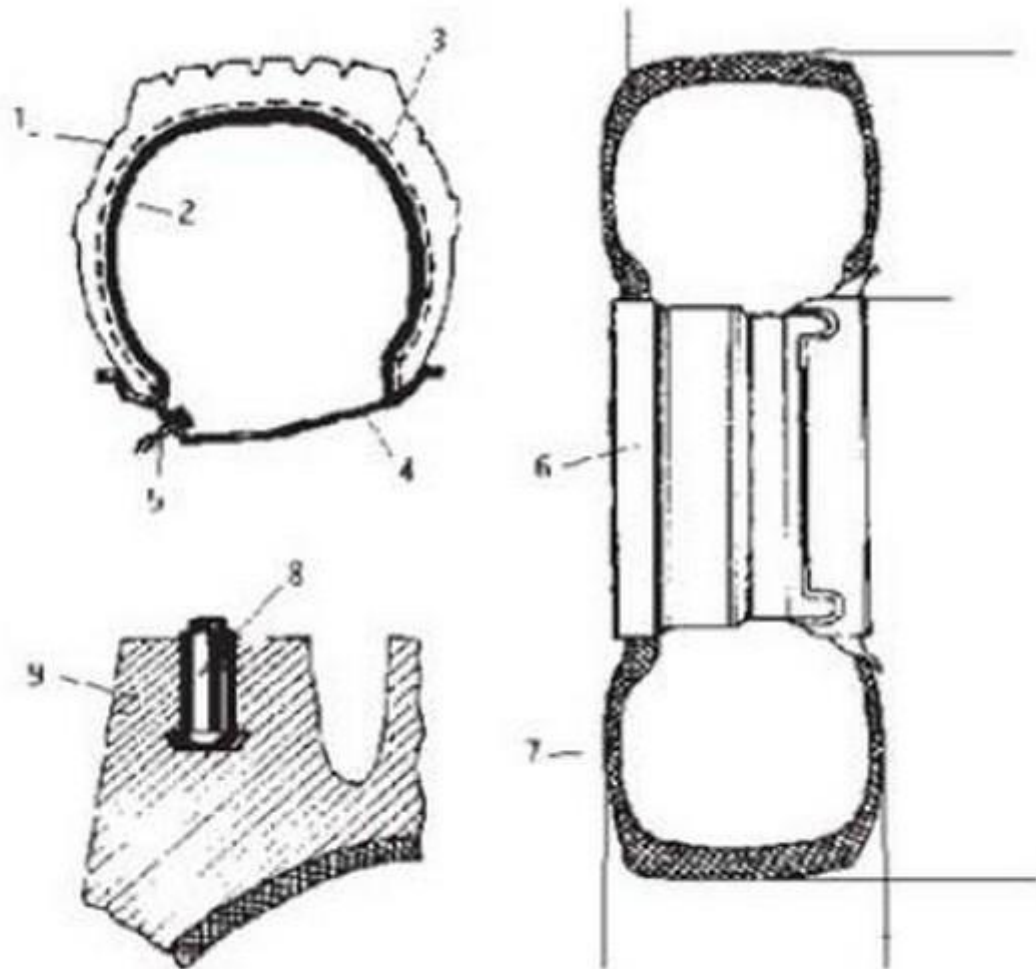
Шина автомобиля: 1 — покрышка; 2 — ездая камера; 3 — корд; 4 — лента обода; 5 — вентиль ездая камеры; 6 — обод; 7 — покрышка; 8 — шип противоскольжения; 9 — шипованная шина. А — ширина протектора; Б — наружный диаметр; В — внутренний диаметр; Г — ширина профиля
